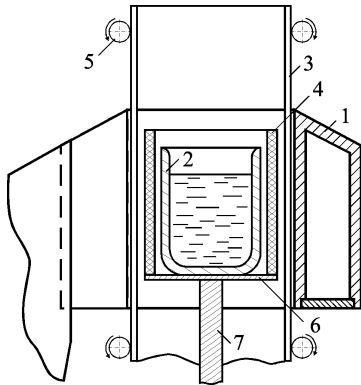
Робочий індуктор концентратора з обладнанням для металізації трубок
